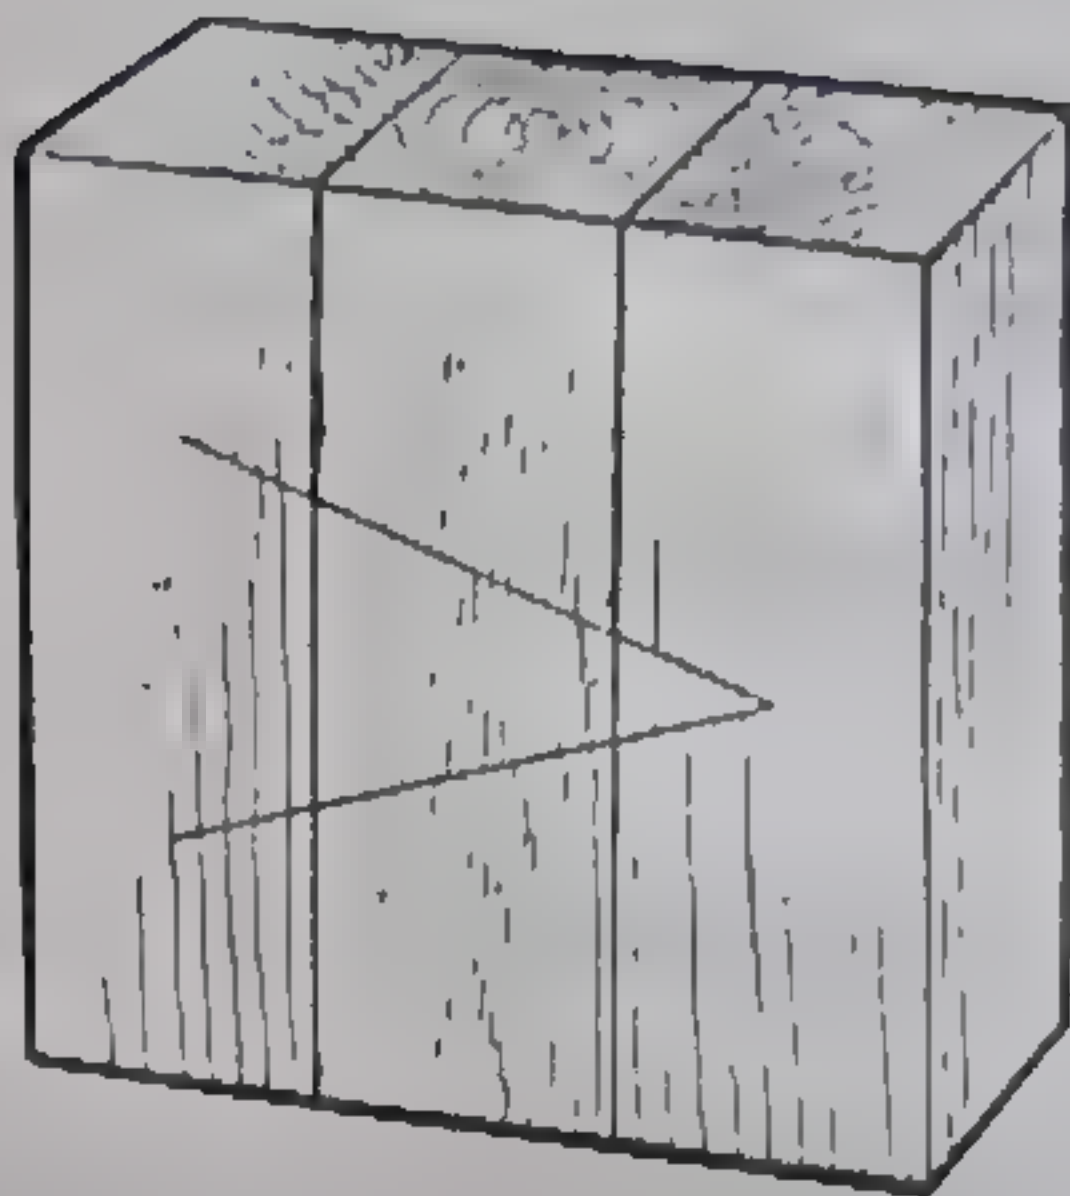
Разметка деталей перед соединением на круглых шипах.
